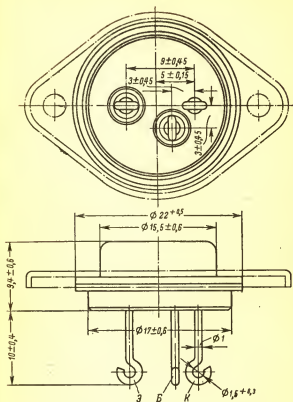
Габаритный чертеж транзисторов П302—П304.
